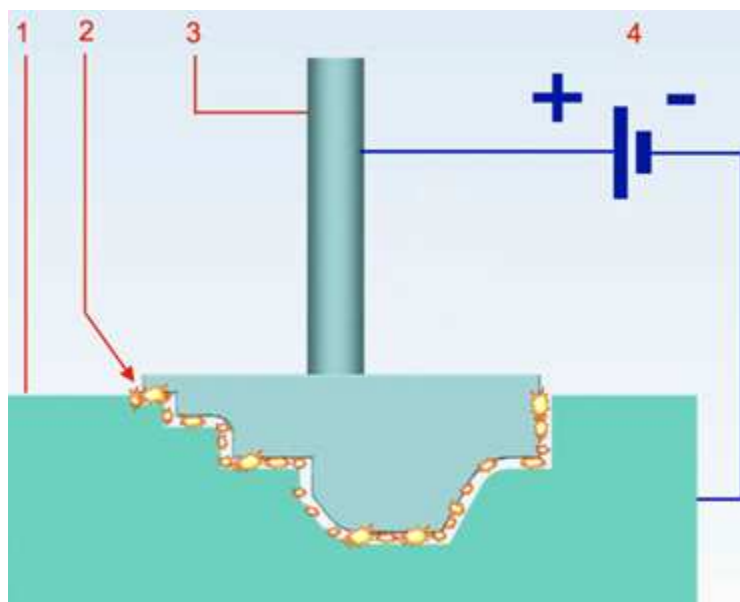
Схема электроэрозионной обработки профильной поверхности (включение на обратную полярность): 1 – обрабатываемая заготовка; 2 – электрические разряды в зазоре между заготовкой и инструментом; 3 – инструмент; 4 – генератор униполярных импульсов
